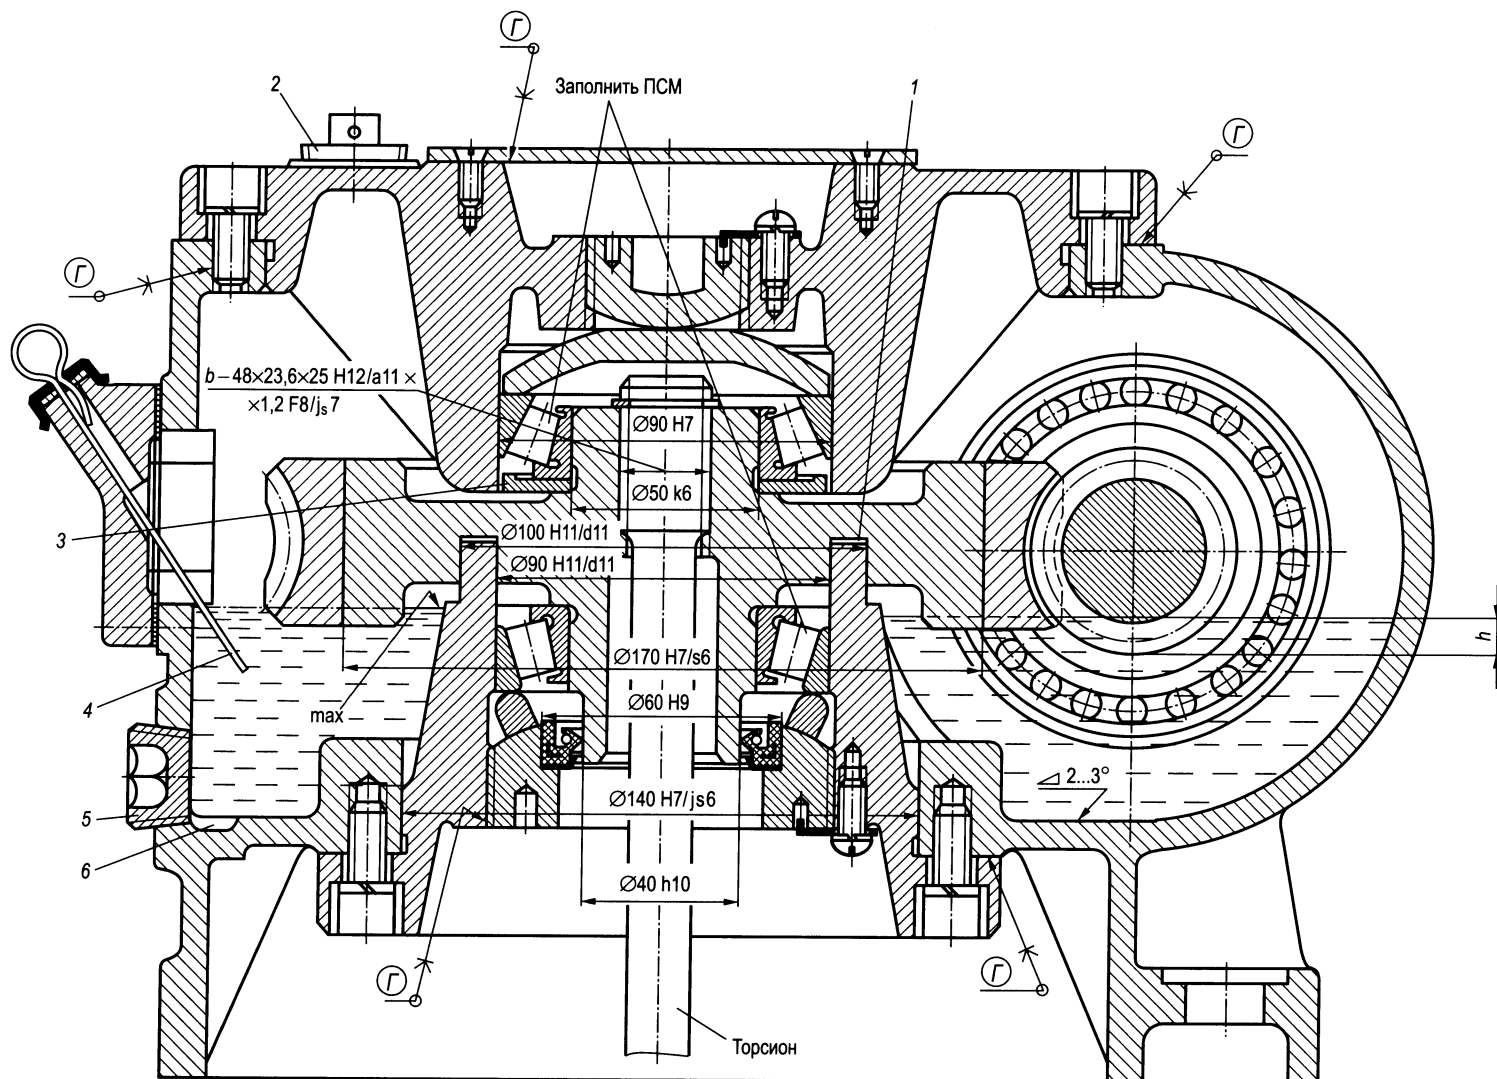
Червячный редуктор с вертикальной осью червячного колеса и погружением червяка в масляную ванну на глубину $h = 3m$:
